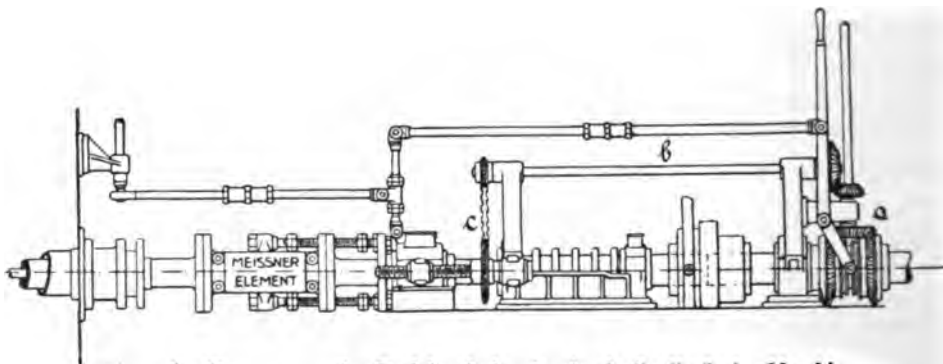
Umsteuerung der Drehflügelschraube durch die Kraft der Maschine.
